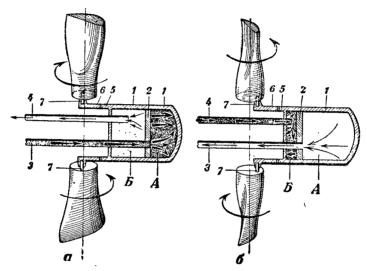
Принцип действия втулки ВИШ двусторонней схемы. Неподвижный поршень и подвижный цилиндр. 1—подвижный поршень; 3 и 4—каналы; 5—поводок; 6—шатун; 7—палец.
